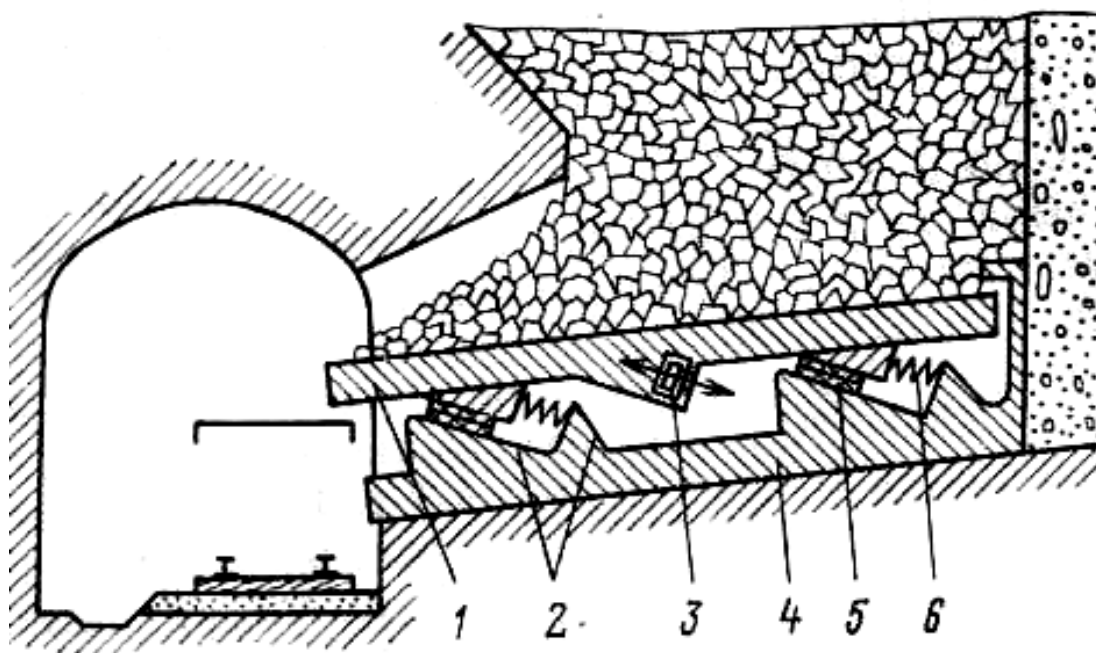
Принципиальная схема ВДПУД-6: 1 — лоток; 2 —выступы; 3 — вибратор; 4 - рама; 5 — резиновая пластина; 6 — пружина
